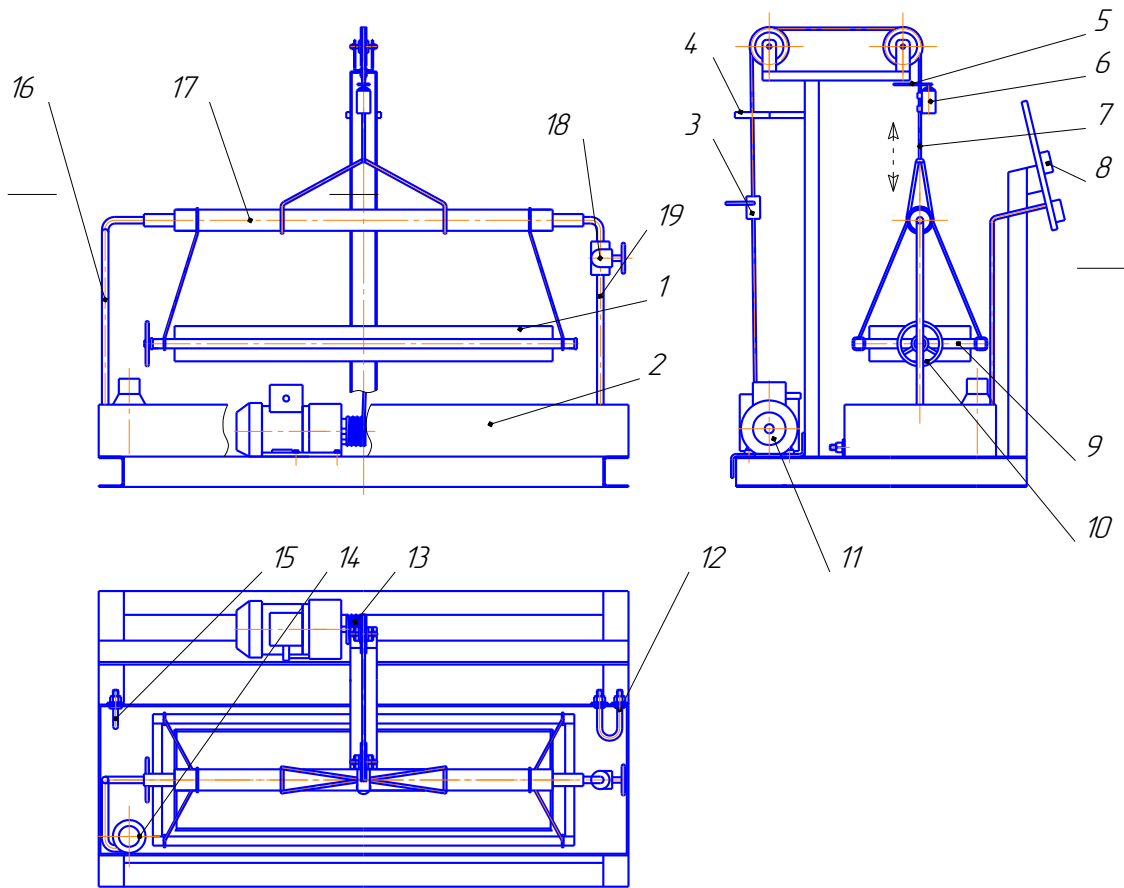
Установка для проращивания зерна: 1 – решето; 2 – ванна; 3 – выключатель концевой рычажковый; 4 – кольцо; 5 – лист; 6 – выключатель концевой кнопочный; 7 – трос; 8 – пульт управления; 9 – рама; 10 – вороток; 11 – мотор-редуктор; 12 – трубчатый электронагреватель; 13 – катушка; 14 – насос; 15 – датчик температуры; 16 – трубопровод нагнетательный; 17 – трубка для орошения; 18 – кран регулировочный; 19 – трубка сливная
